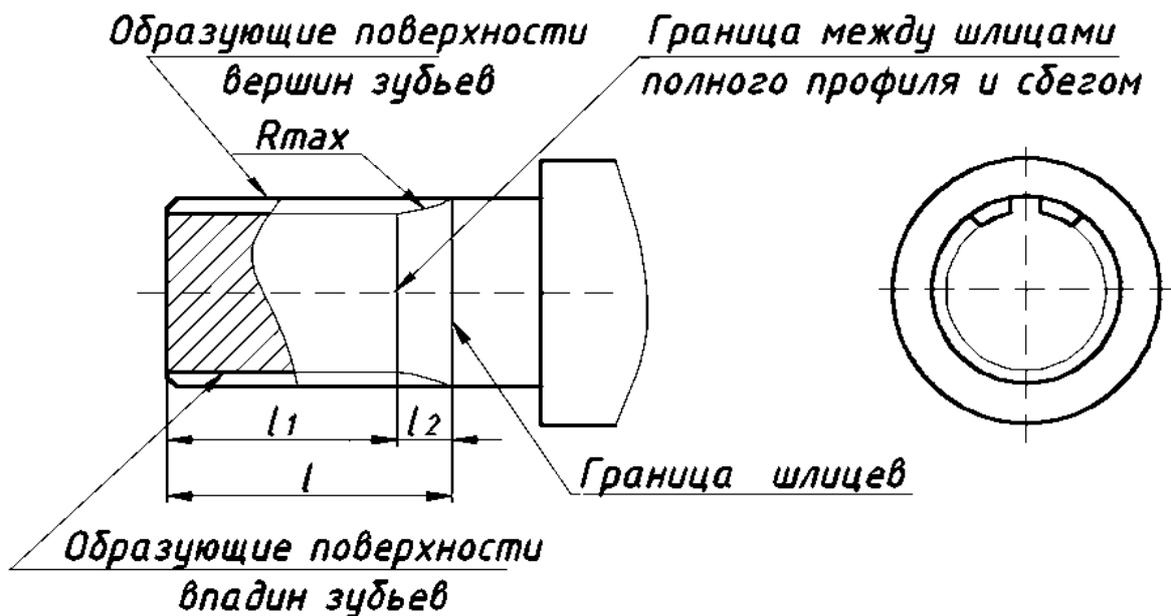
Образец условного изображения шлицев: l — полная длина зубьев; l_1 — длина зубьев полного профиля; l_2 — длина сбега; R_{max} — наибольший радиус инструмента (фрезы)
